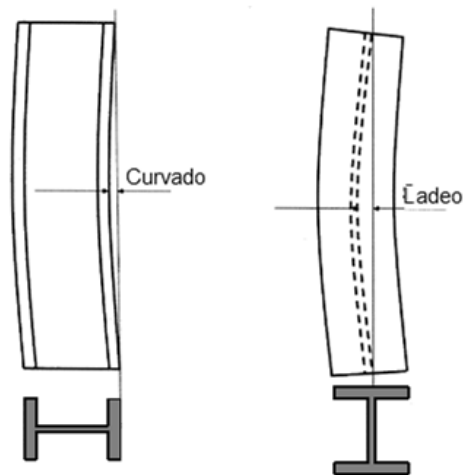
Tolerancias de producción en la planta metalúrgica para las dimensiones de una sección transversal
